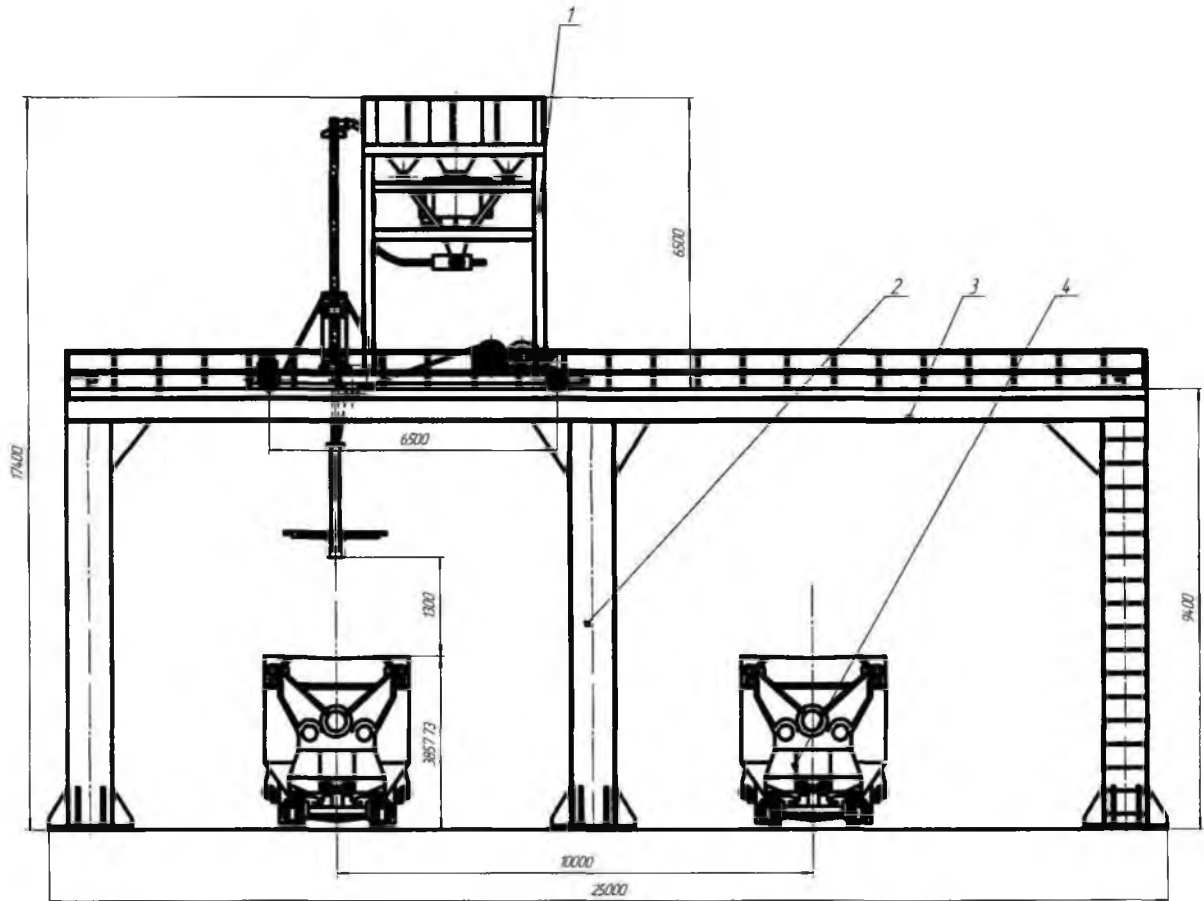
Пристрій установки для поготовки і подачі порошків в чавуновозний ківш
